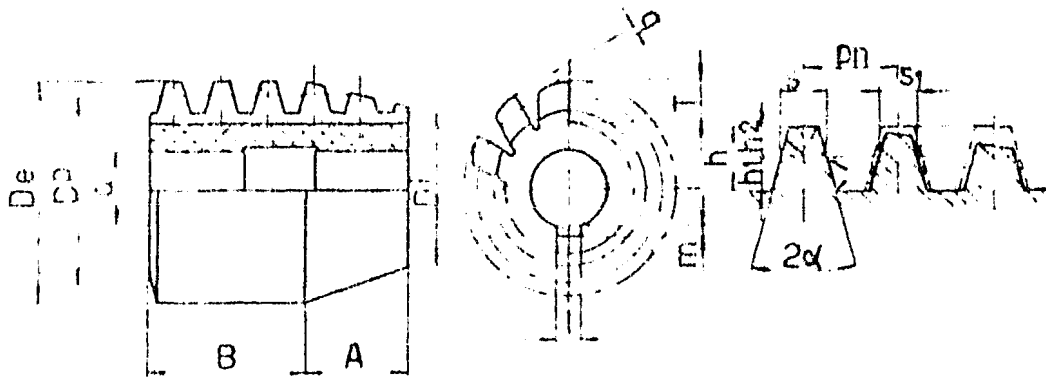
Fresa-tornillo para el tallado de dientes helicoidales de ruedas cilíndricas.
